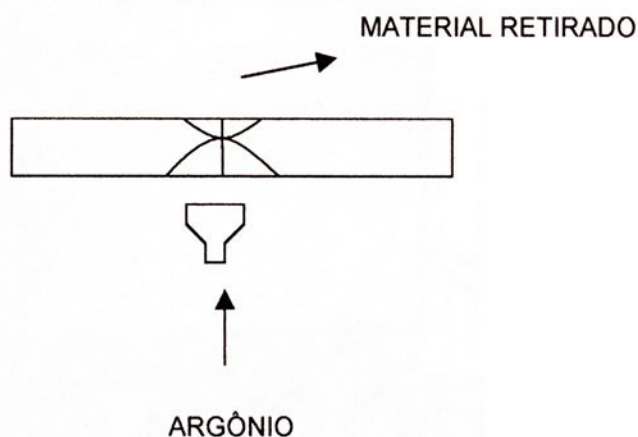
Posição na junta soldada a ser protegida da oxidação do metal com argônio, durante a operação de soldagem.
